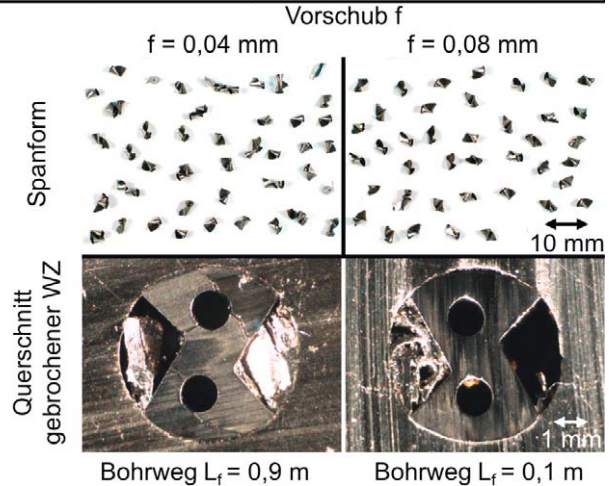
Spanform und Querschnitt gebrochener Werkzeuge.
